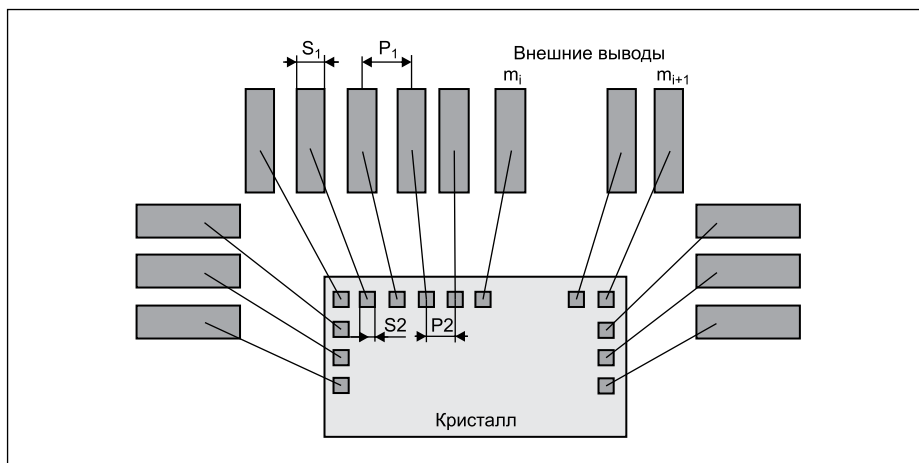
Схема проволочных межсоединений между контактными площадками кристалла и корпуса прибора
